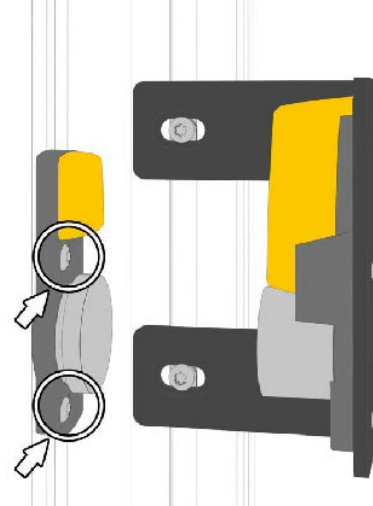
Ankerplatte am Profil der Schiebetüre anbringen, zur Prozesszuhaltung ausrichten und zur Prozesszuhaltung ausrichten. Schrauben M6 x 16 mm Torx festziehen.
